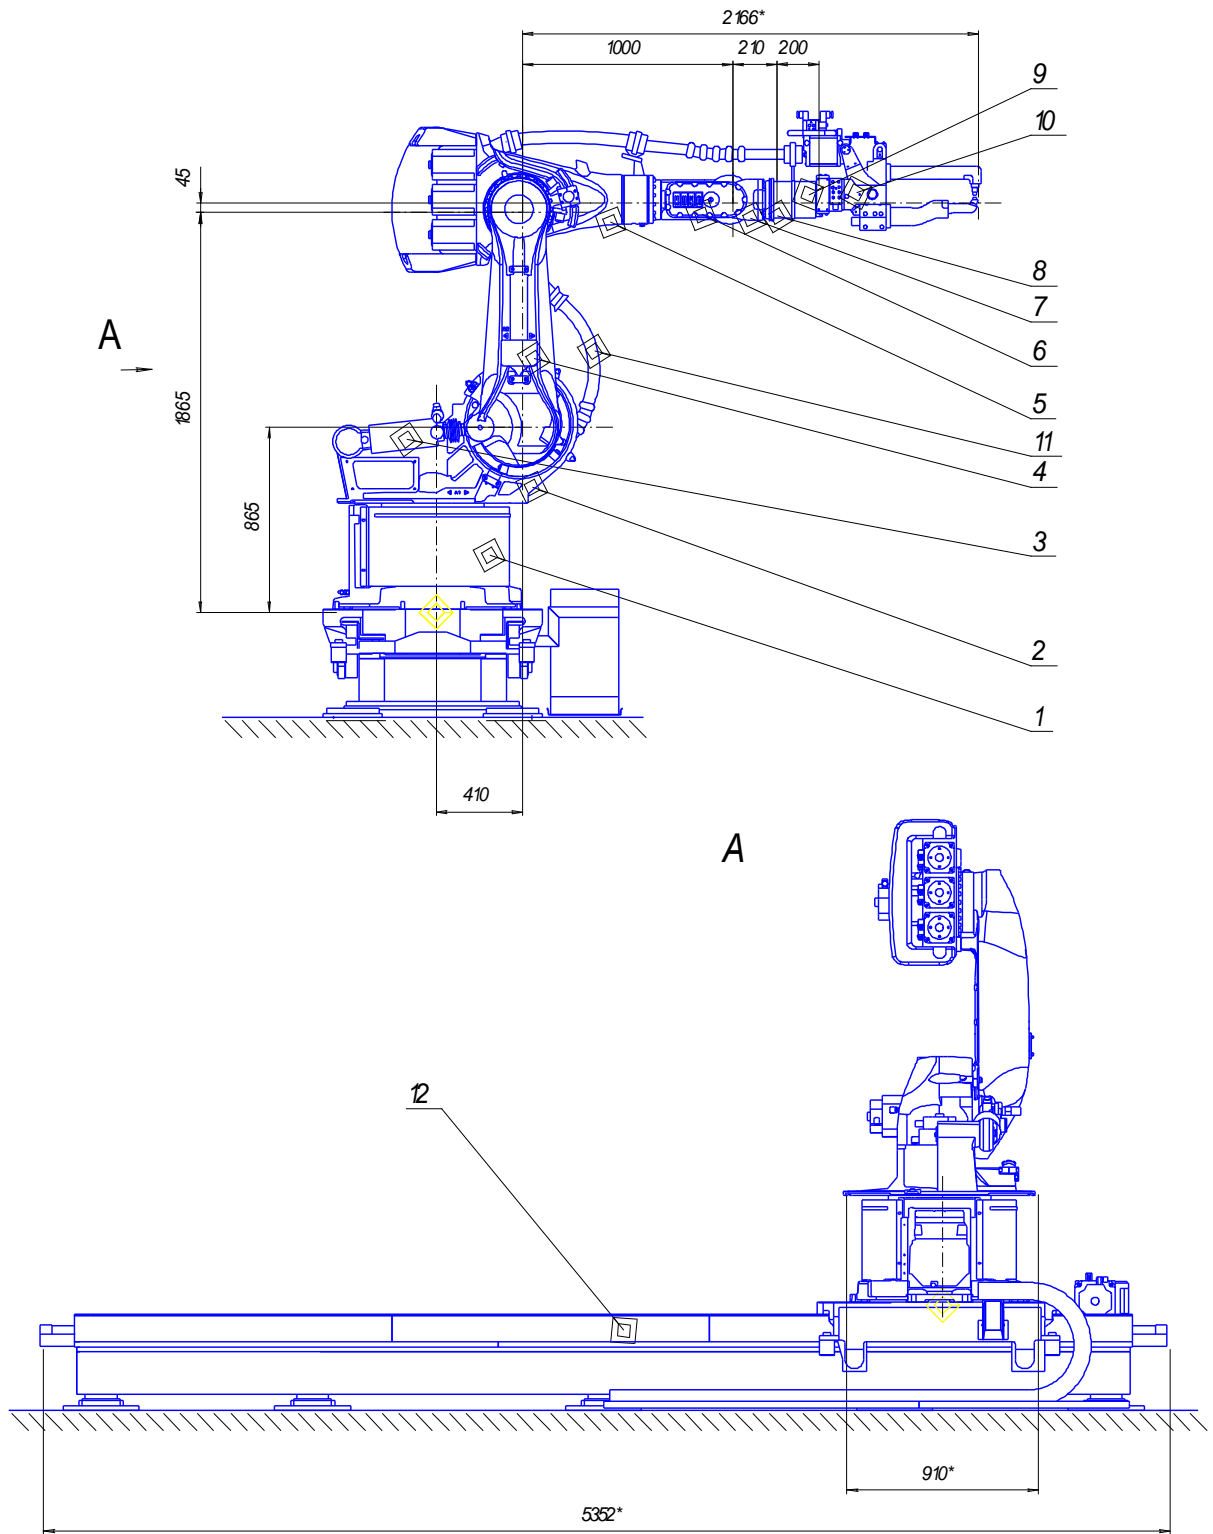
Манипулятор комплектации №2 с X-образными сварочными сервоклещами
